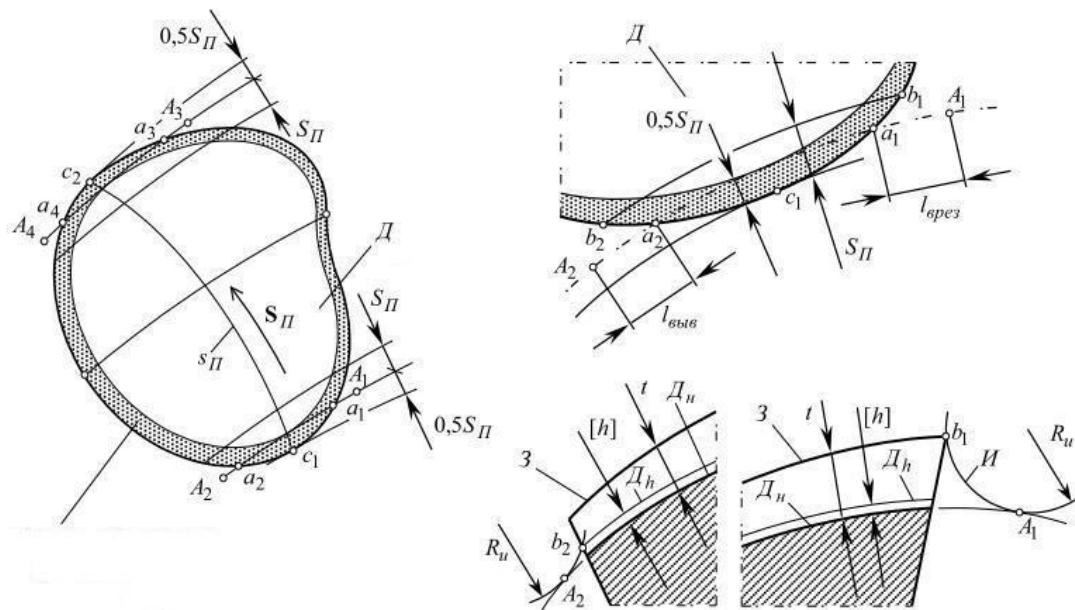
Визначення положення крапки початку обробки складної поверхні деталі на багатокоординатному верстаті з ЧПК
